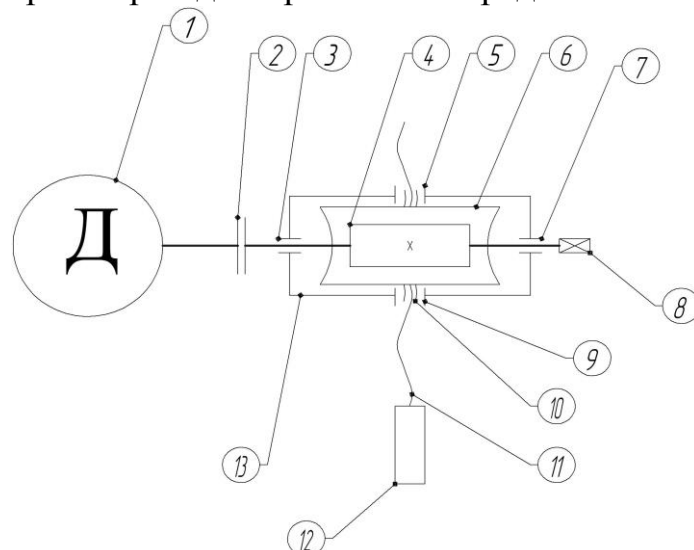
Кінематична схема привода з черв'ячною передачею:
